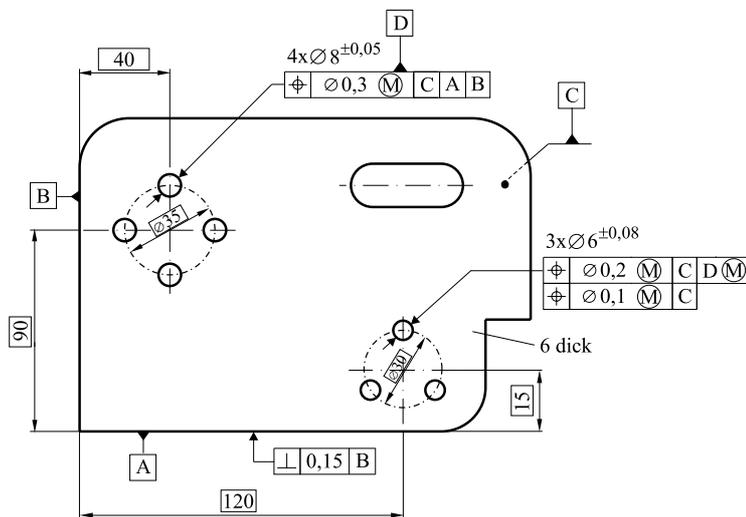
3-D-Bezug an einem Bauteil unter Einbezug einer Formelementgruppe
